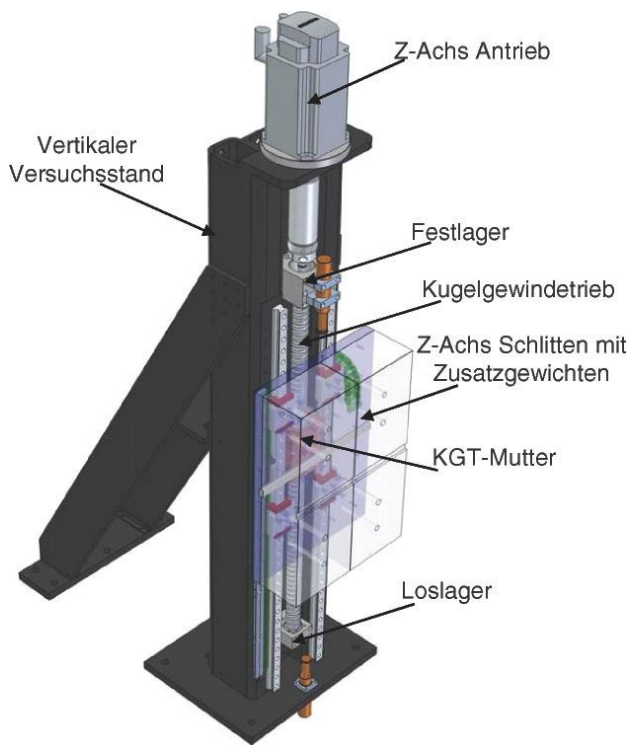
Vertikaler Versuchsstand für Kugelgewindetriebe
